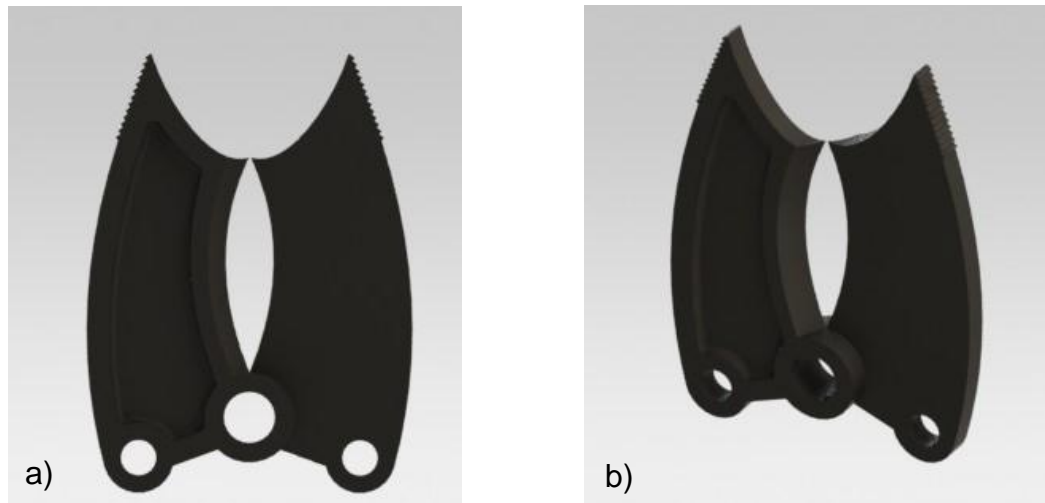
Herramienta de corte adaptable a “spreader” a) Vista frontal y b) Vista isométrica.
